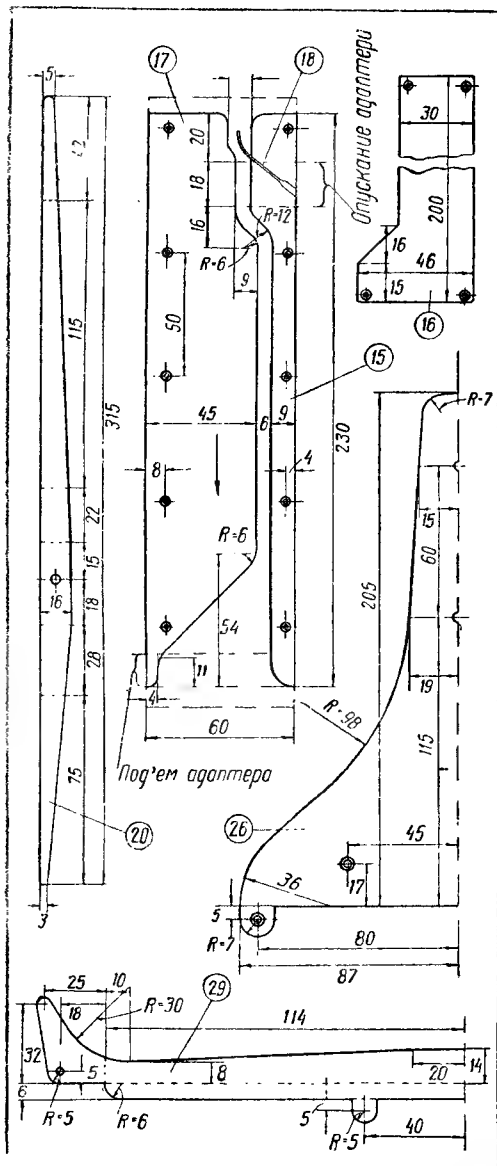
Крупные детали автомата, изготовленные из листового металла
